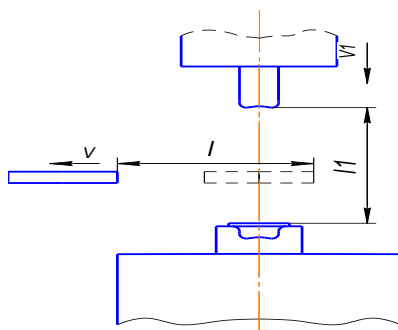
Схема рабочей зоны прессы при штамповке с радиальным нагревом.
